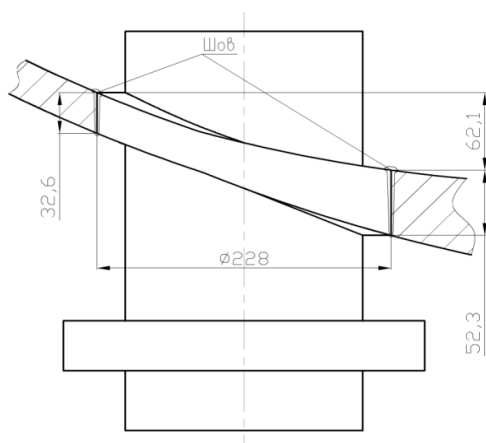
Конструкция сварного стыка патрубка Ø228 мм
